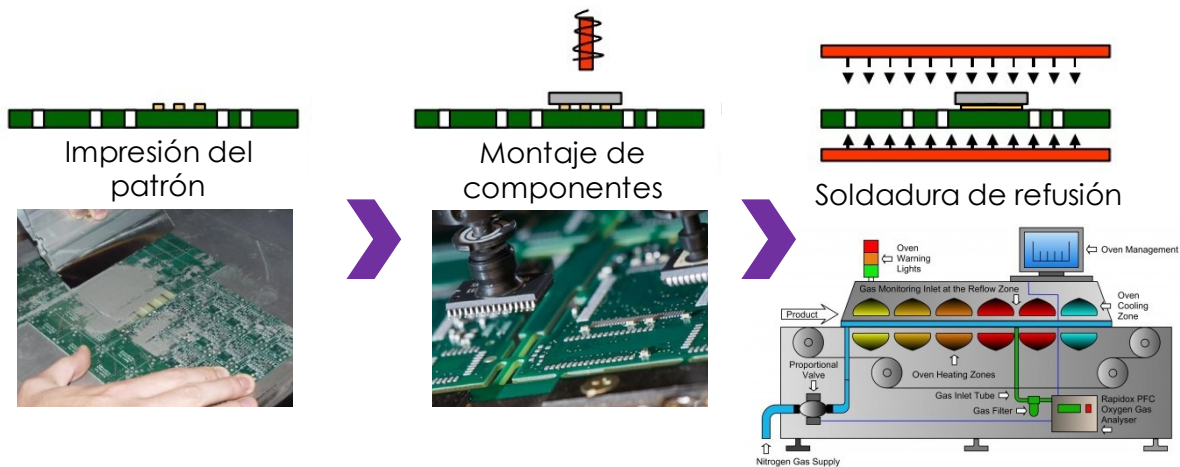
Etapas del proceso en la soldadura de refusión.
